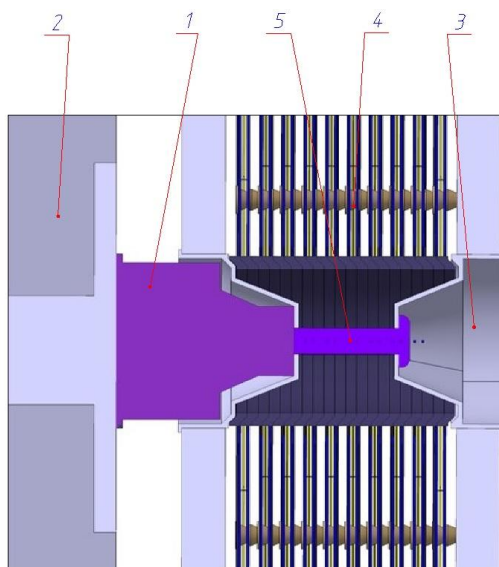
Схема удерживающего механизма: 1 – механическая часть; 2 – корпус КА; 3- воронка; 4- пакет панелей БС; 5- штырь
